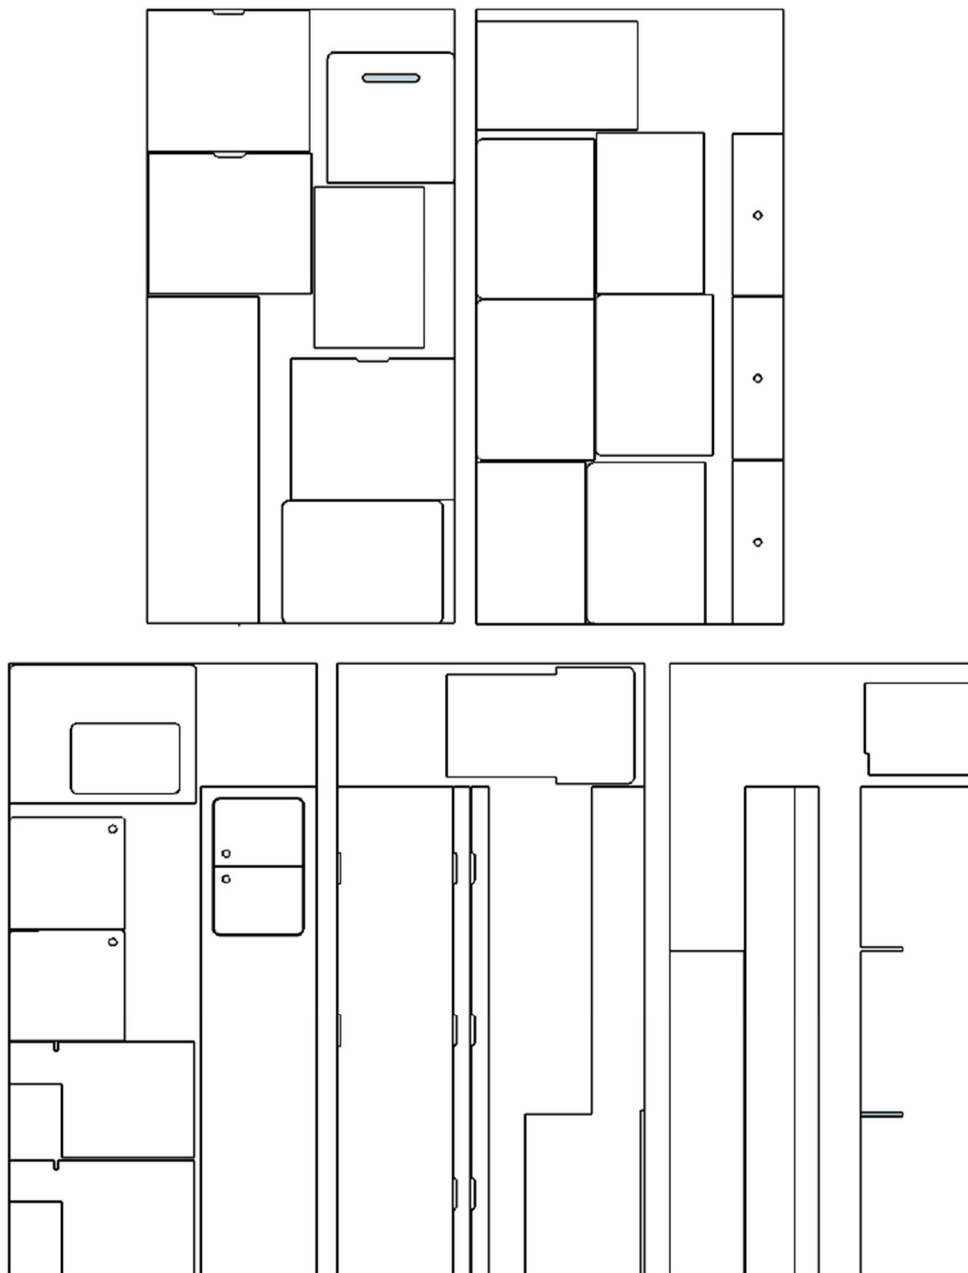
Planificação de corte de peças estruturais do módulo para corte em CNC Fonte: Desenho do autor
